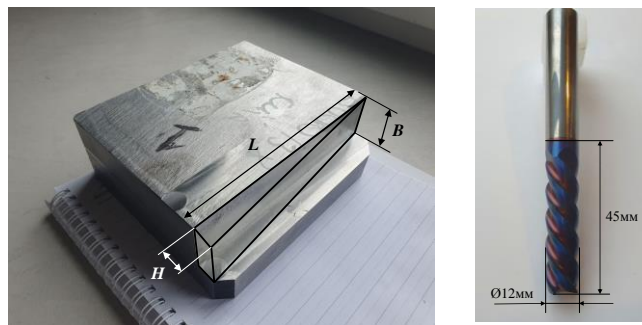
Оброблена деталь (контур припуску заготовки виділений лініями) і фреза
